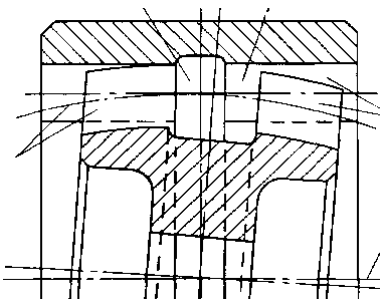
Зубчатая муфта с кольцевыми канавками, разделяющими зубчатые венцы втулки и обоймы на две части
